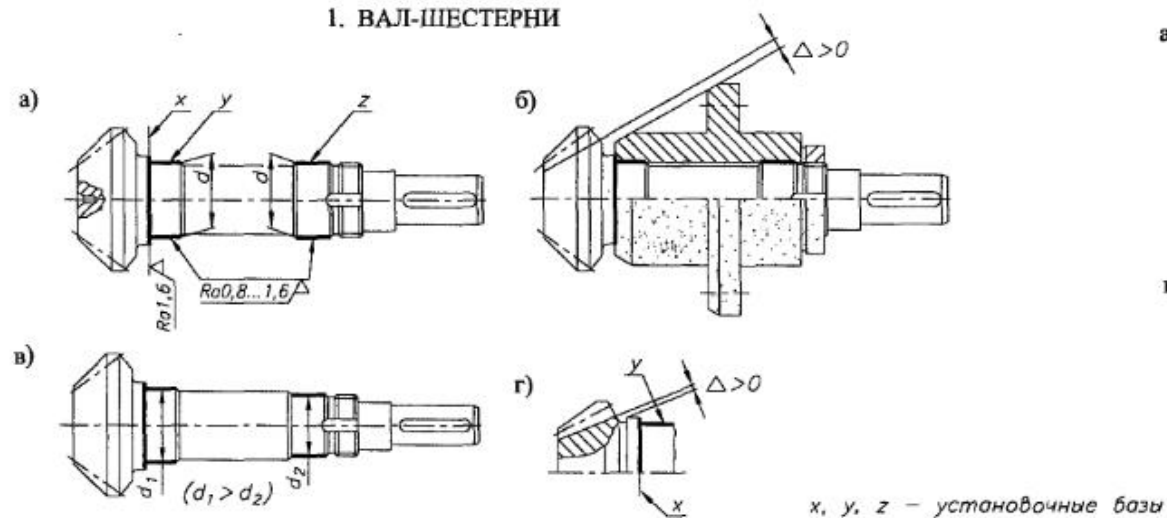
Установочные базы для нарезания зубьев на вал-шестернях
